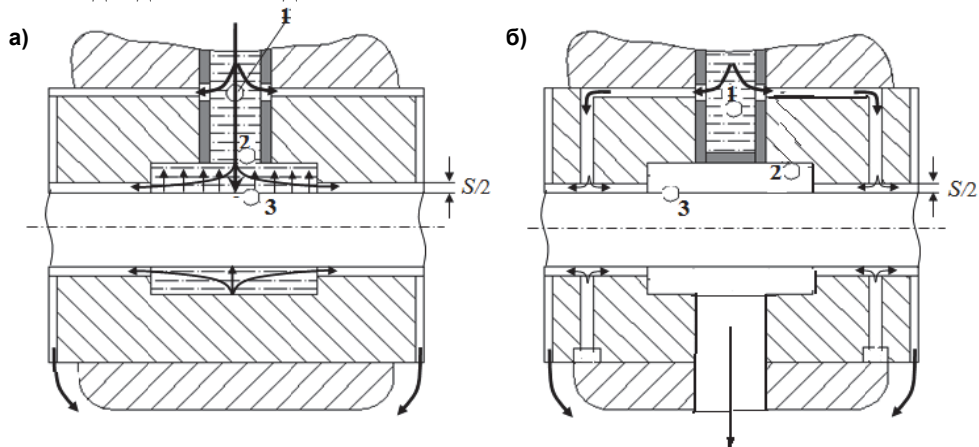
Схема подшипникового узла: а – серийного; б – предлагаемого
